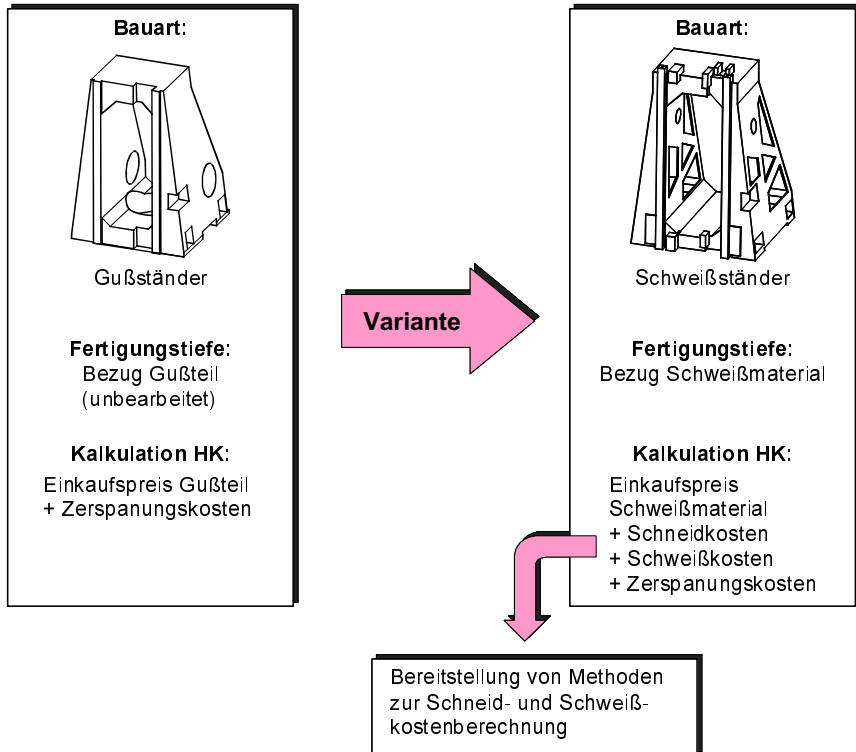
Bildung einer Schweißständervariante
